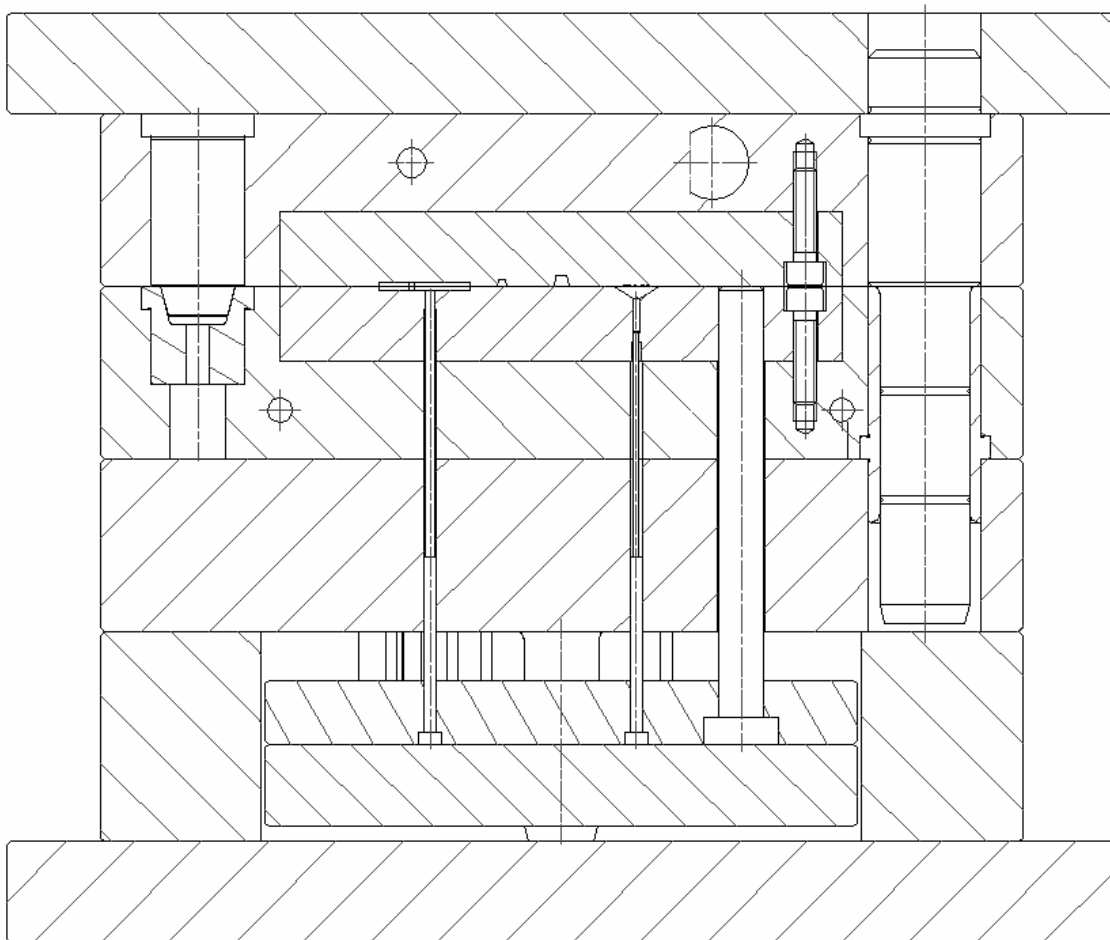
Molde para injetar a unidade representativa de 16 cadeias laterais: desenho técnico em corte da montagem
